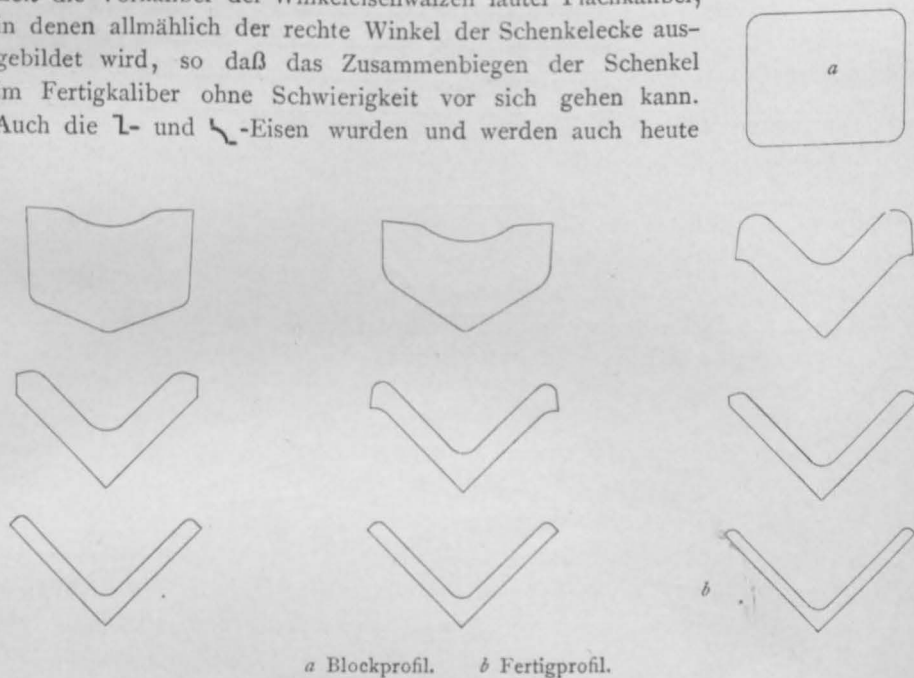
Umrisse der Walzenfurchen (Kaliber) für das Walzen der Winkeleisen.
